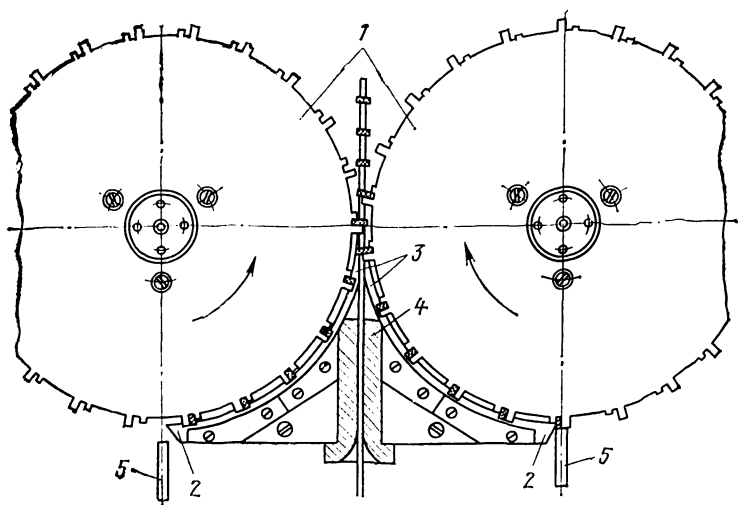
Диски для насадки шайб и разрезные ножи (вид сверху).
